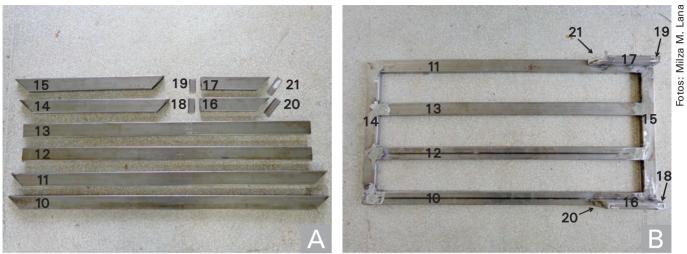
Partes componentes (A) e montagem do encosto (B), Embrapa Hortaliças, 2014.
